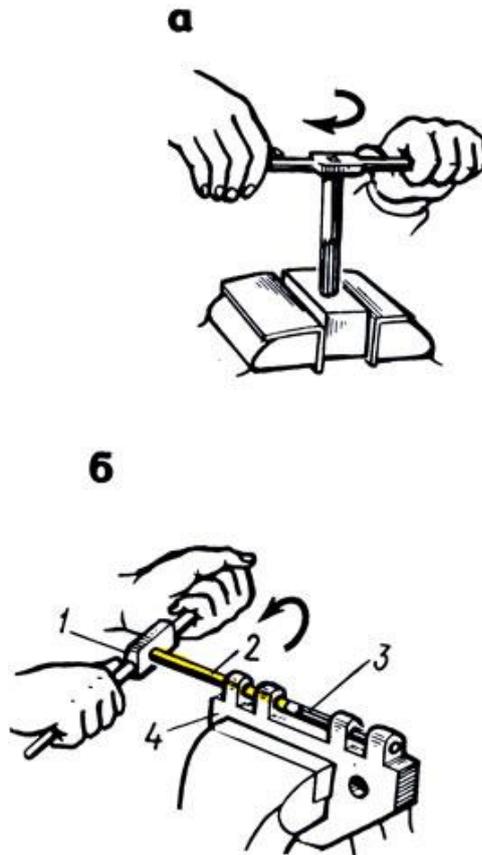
Развертывание: а - установка развертки и воротка, б - развертка с удлинителем; 1 - вороток, 2 - удлинитель, 3 - развертка, 4 - деталь
